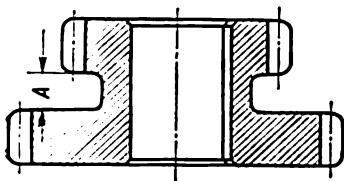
Construction d'une pièce assurant le dégagement de l'outil
